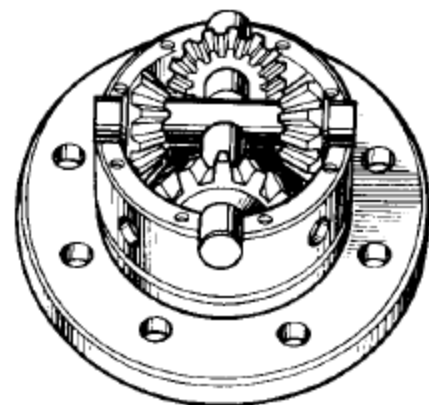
Установка разъёмной крестовины с сателлитами в левую коробку сателлитов
